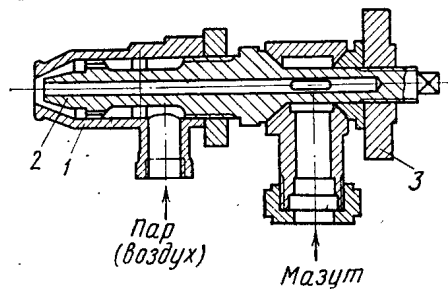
Форсунка высокого давления конструкции В. Г. Шухова:
